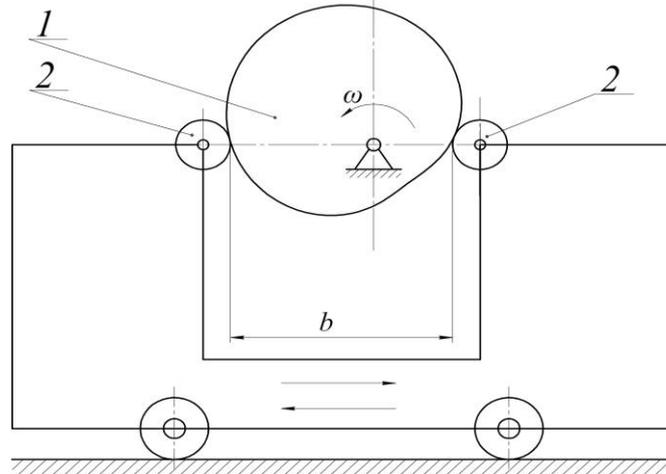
Схема механізму з кулачковим приводом зворотно-поступального руху візка.
